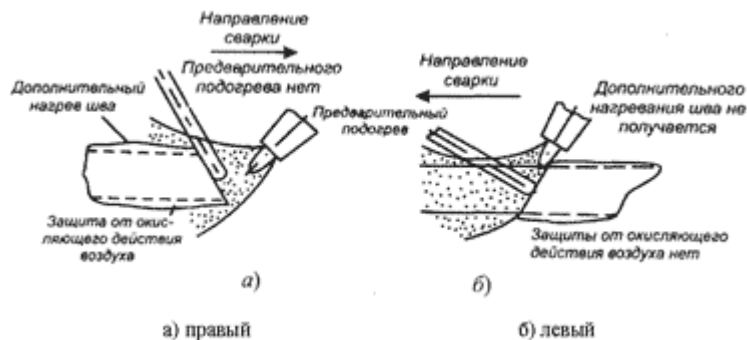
Способы перемещения горелки (способы газовой сварки)
